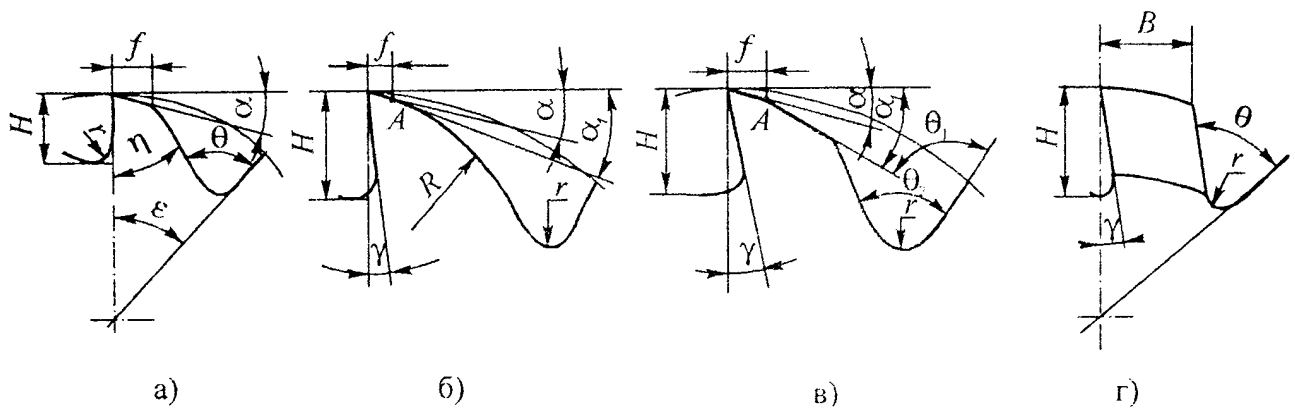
Форма зубьев фрез: а – трапецевидная; б – параболическая; в – усиленная; г – затылованный зуб.
